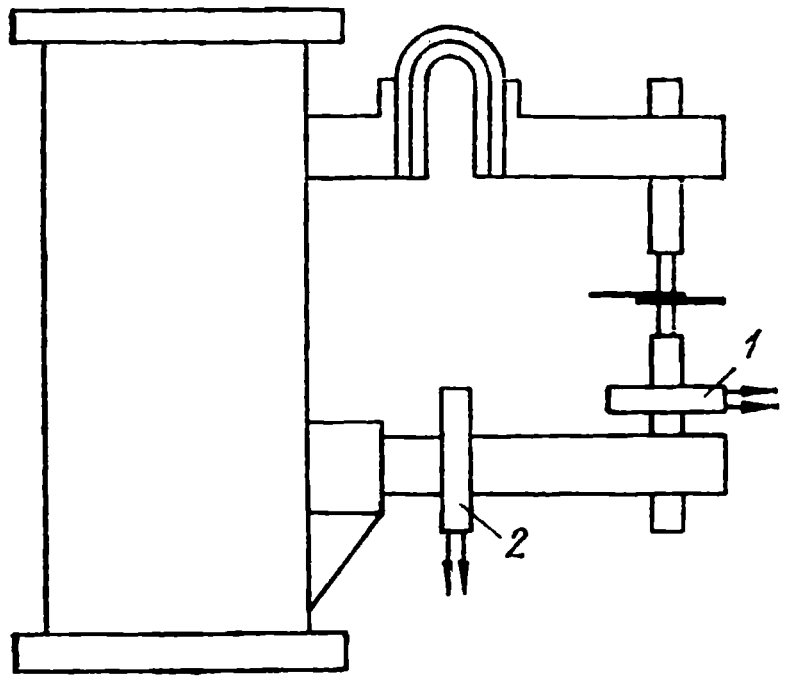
Расположение торонда на сварочной машине:
